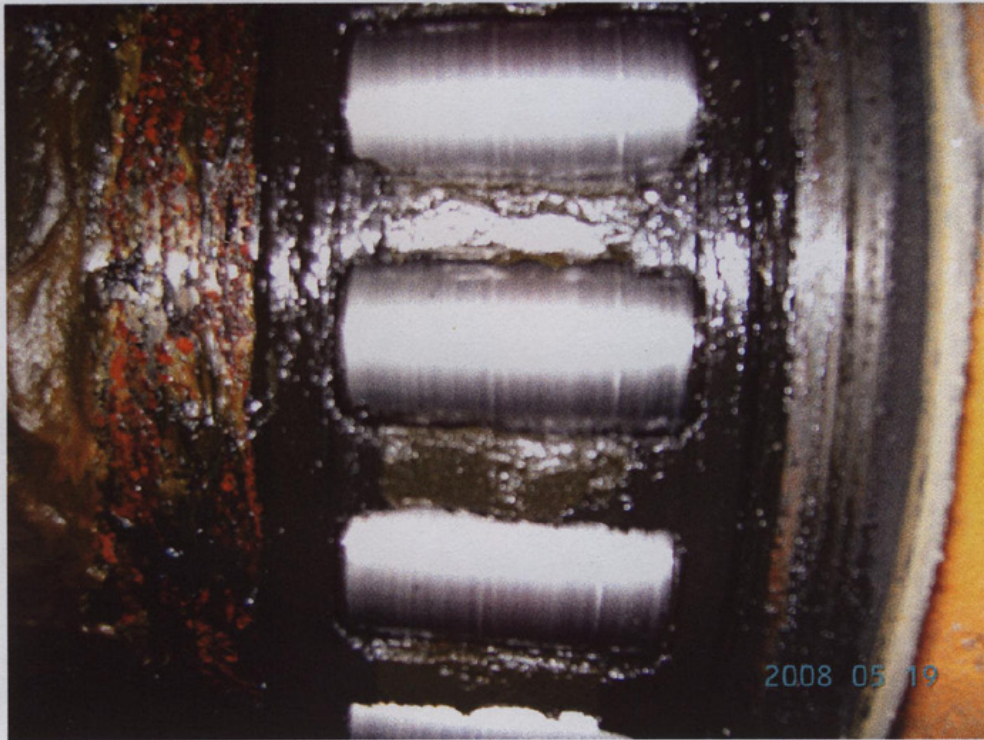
Ролики внутреннего подшипника со смазкой Литол 24.
